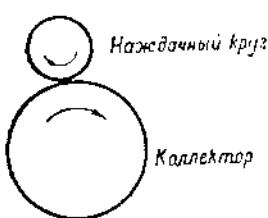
Шлифовка коллектора шлифовальным кругом.
